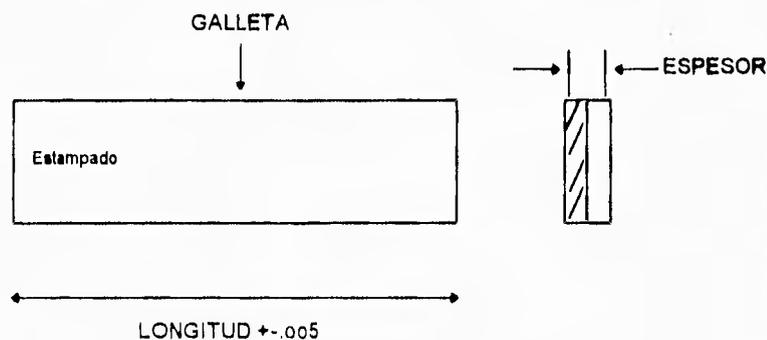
CORTE GALLETA Y ESTAMPADO
